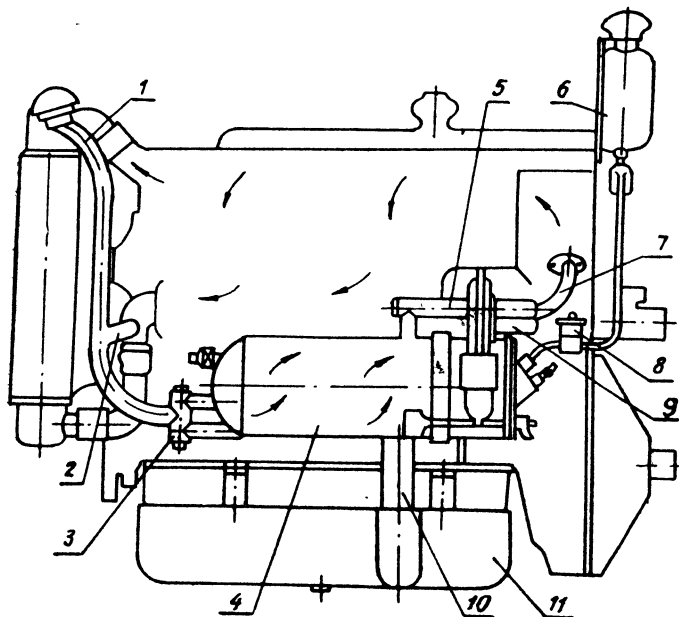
Схема установки подогревателя ПЖБ-32 на двигателе:
